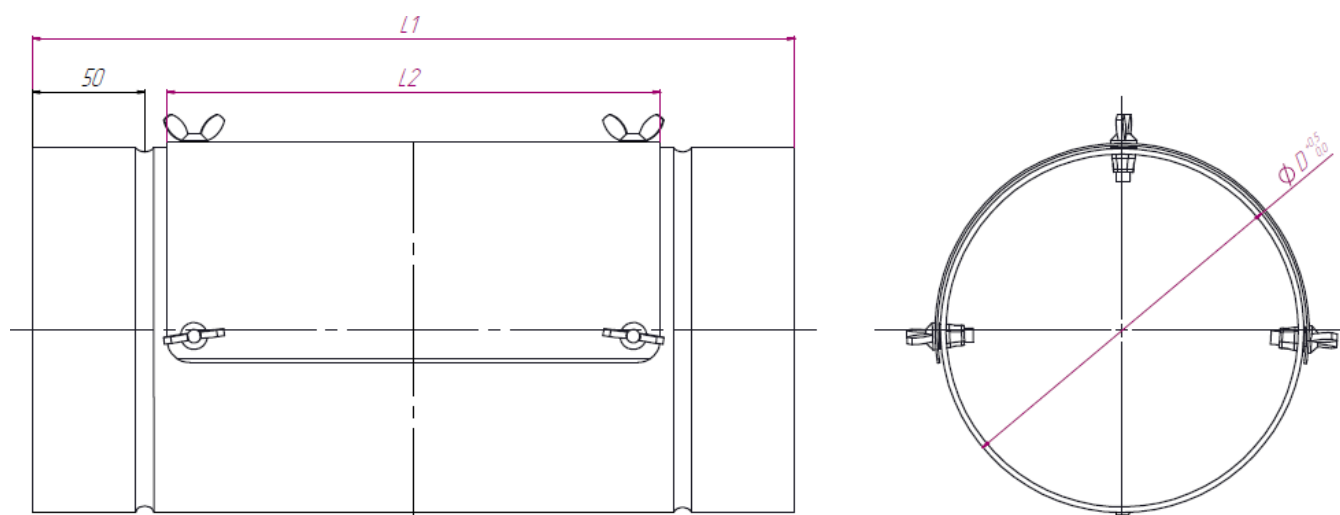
Основные габаритные размеры корпуса ВР-Кр
